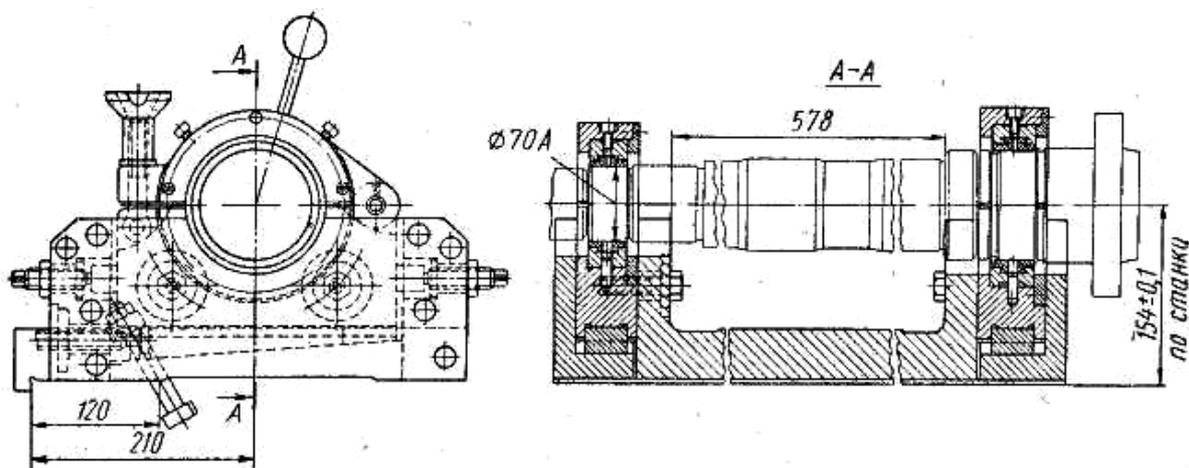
Приспособление для шлифования поверхности осевого конического отверстия шпинделя
